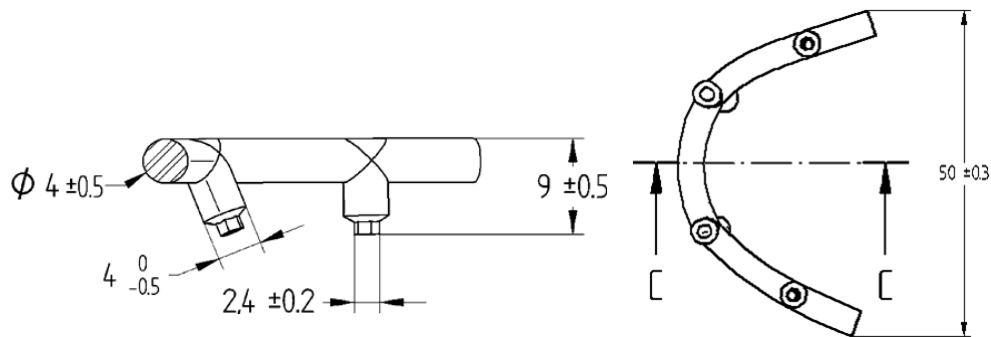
Plano barra tipo 4 (geometría circular), indicando dimensiones clave del modelo.
